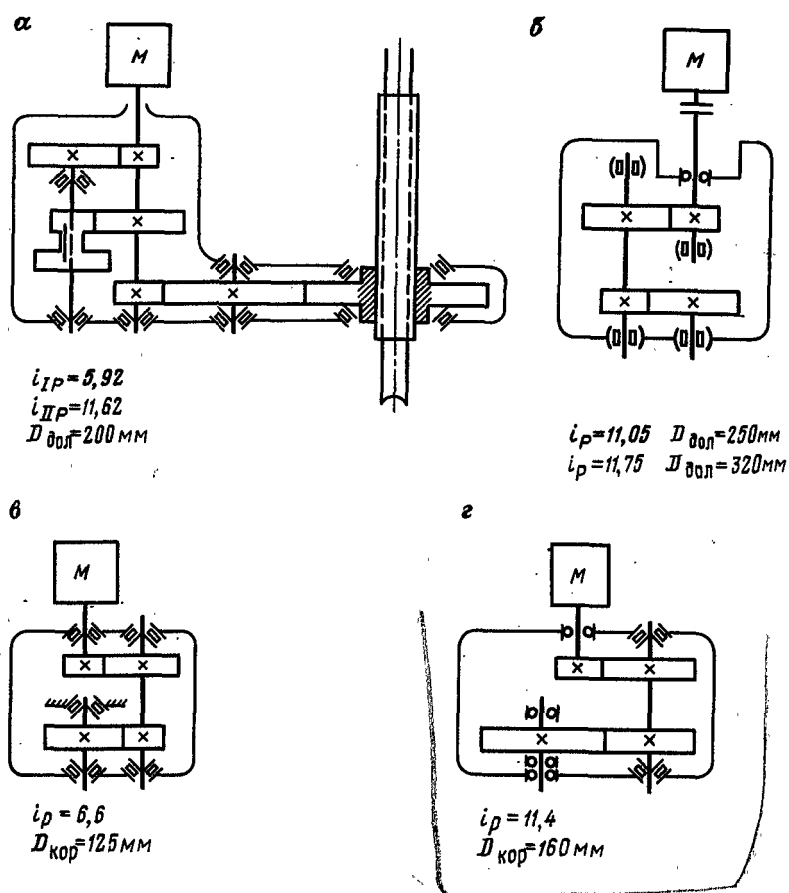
Кинематические схемы привода вращателей бурового инструмента станков
